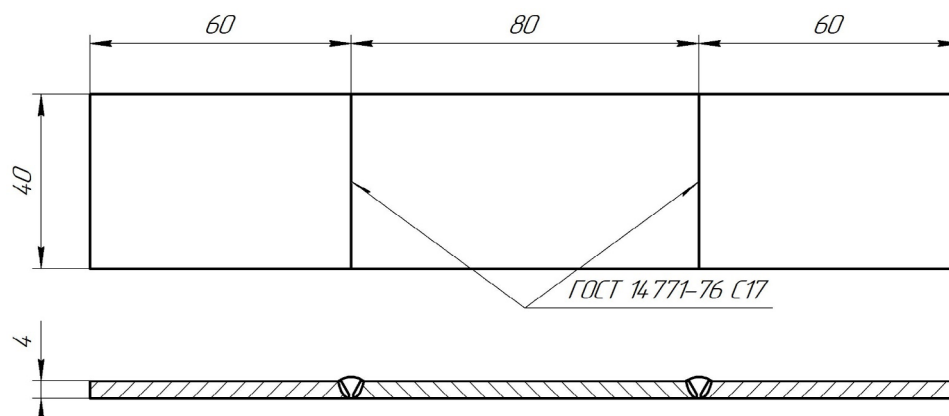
Схема сварки пластин из стали Miilux Protection 500
